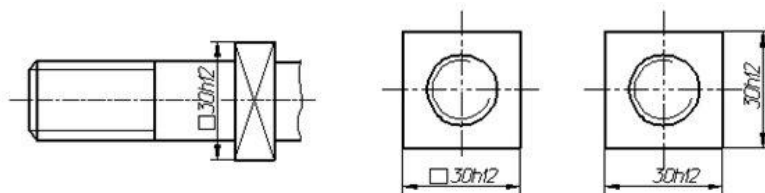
Примеры нанесения размера с использованием знака «квадрат»
